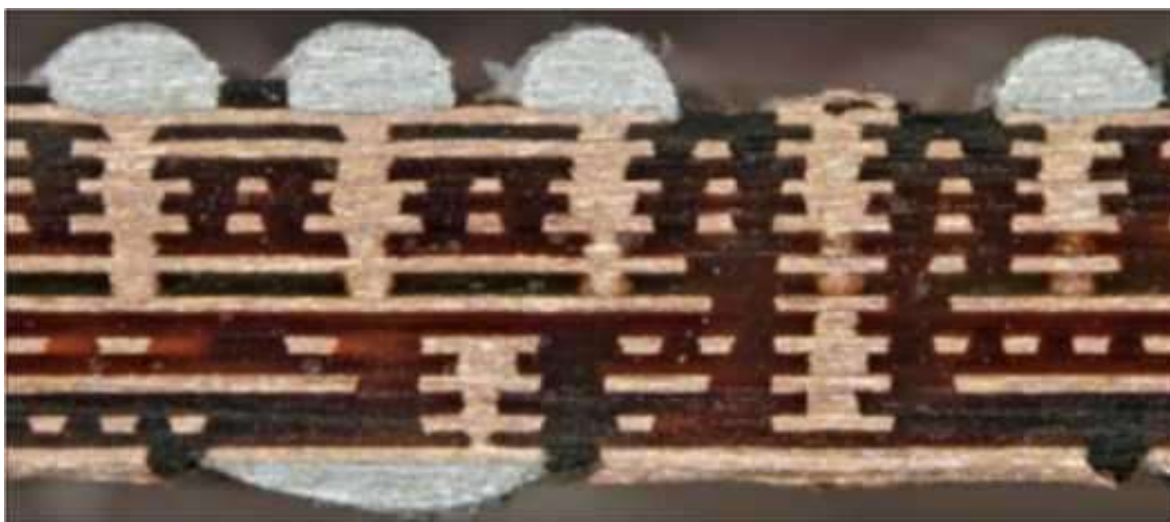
Поперечний переріз багатошарової друкованої плати
